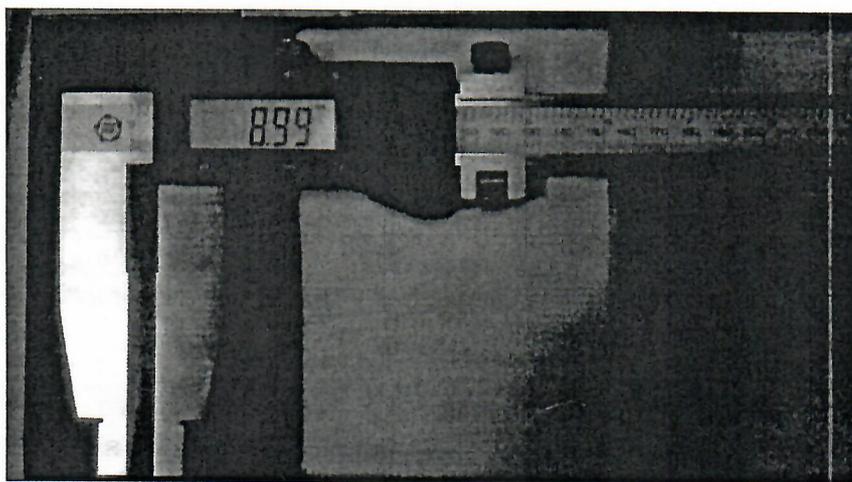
Общий вид штангенциркулей типа ШЦЦ-III.
